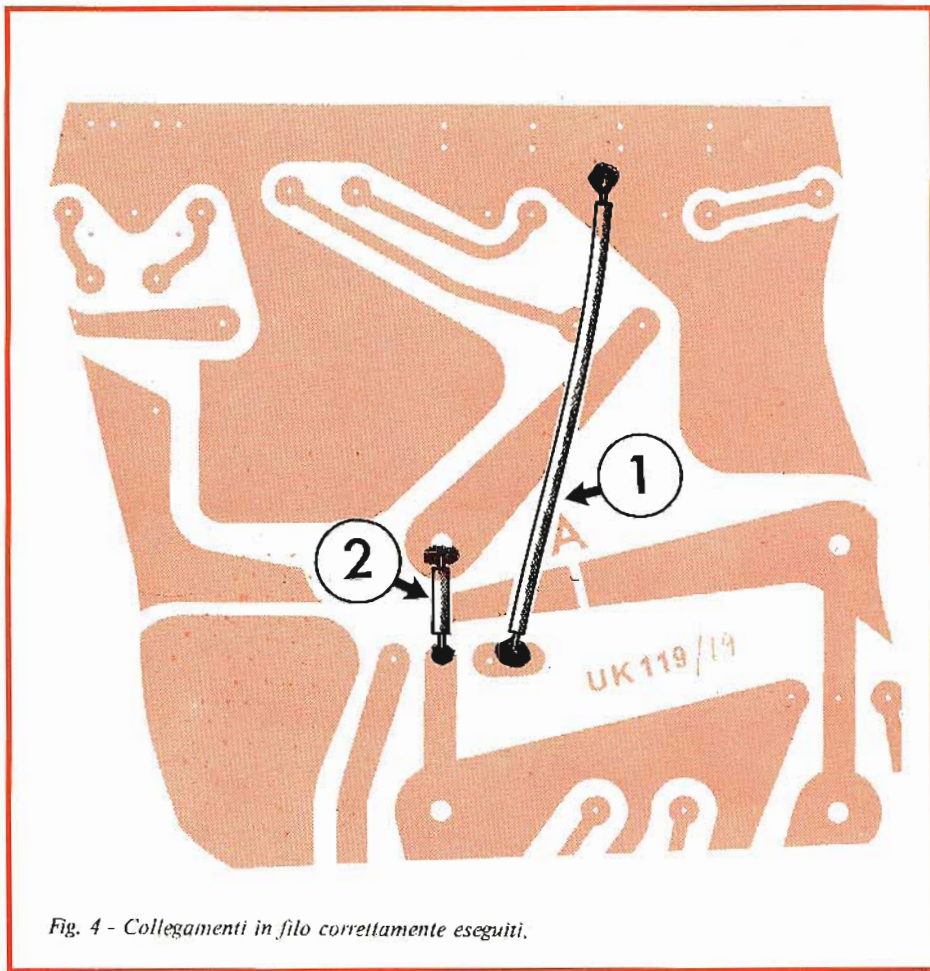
Collegamenti in filo correttamente eseguiti.
